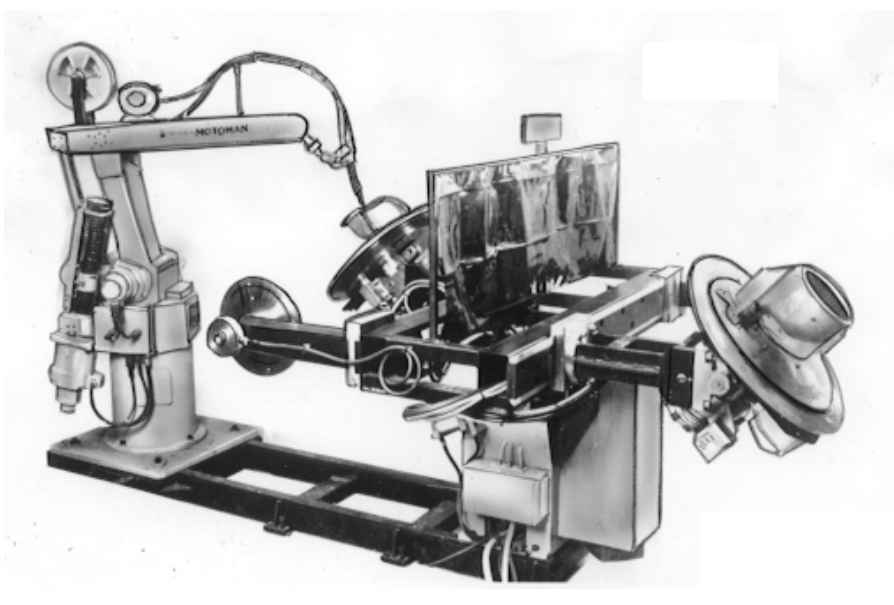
Робототехнический комплекс для дуговой сварки с ПР «Мотоман» с двухкоординатным столом.
